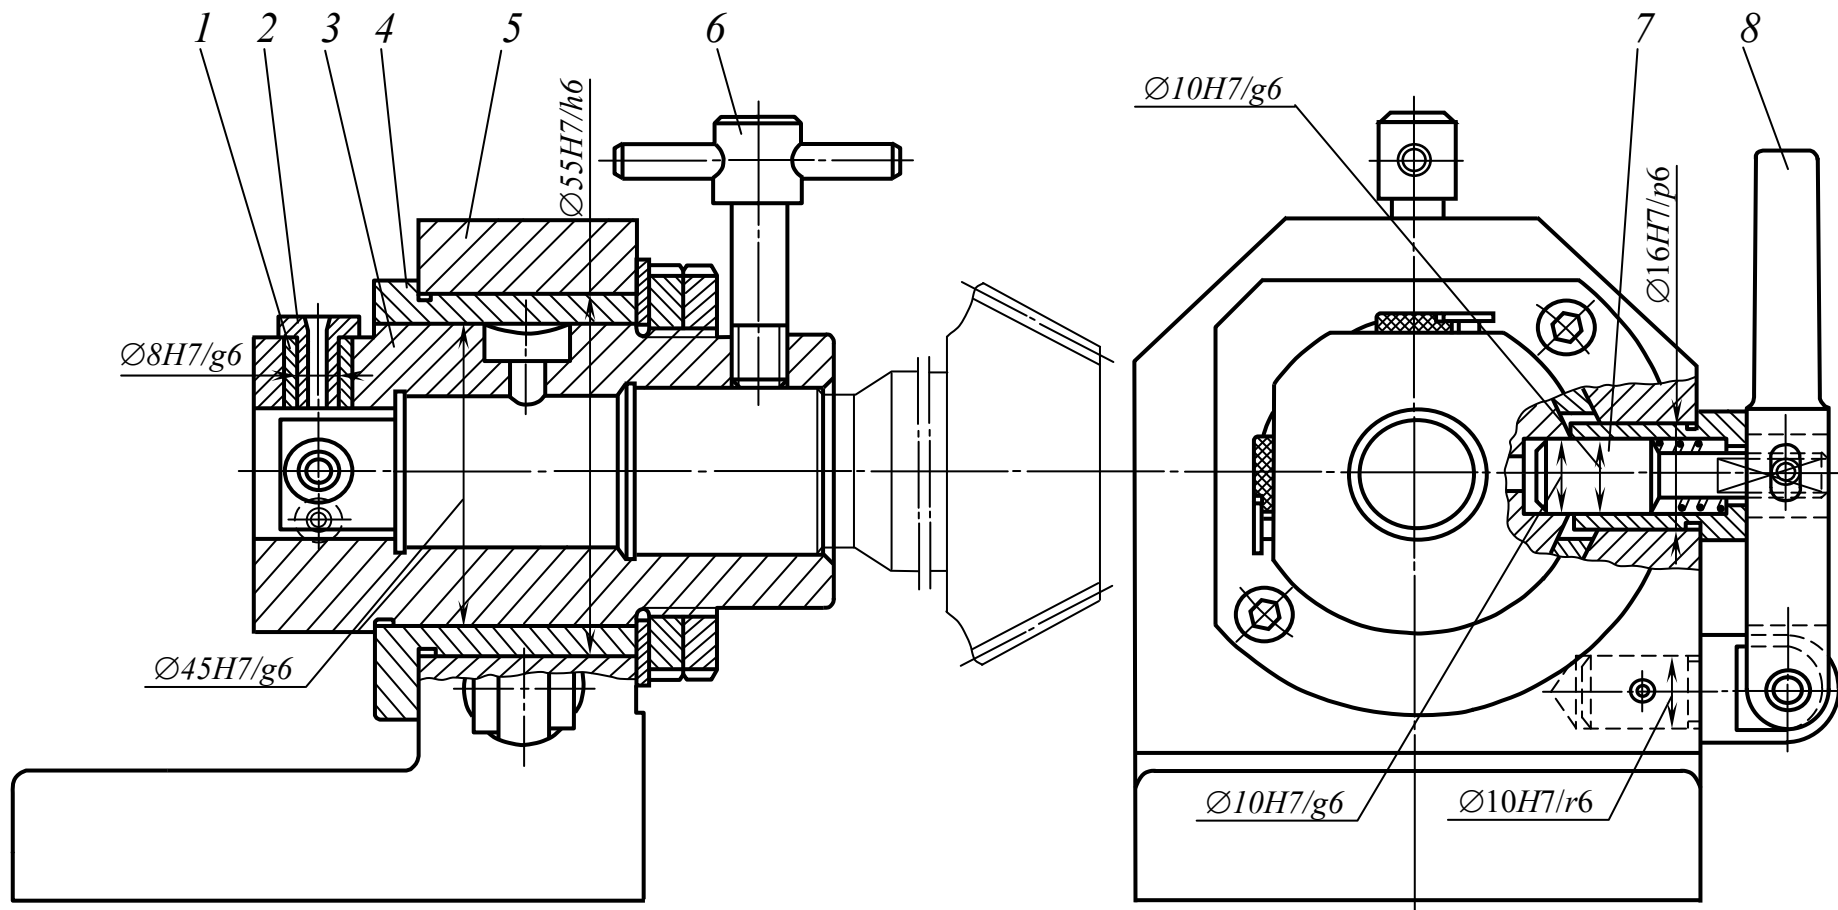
Примеры посадок в соединениях деталей приспособления для сверления:
